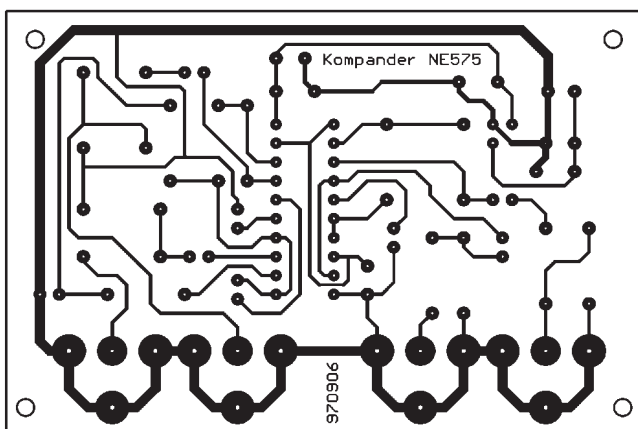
Das Platinenlayout für den Audiosignal-Kompander ist ebenfalls auf einseitigem Material ausgeführt.
